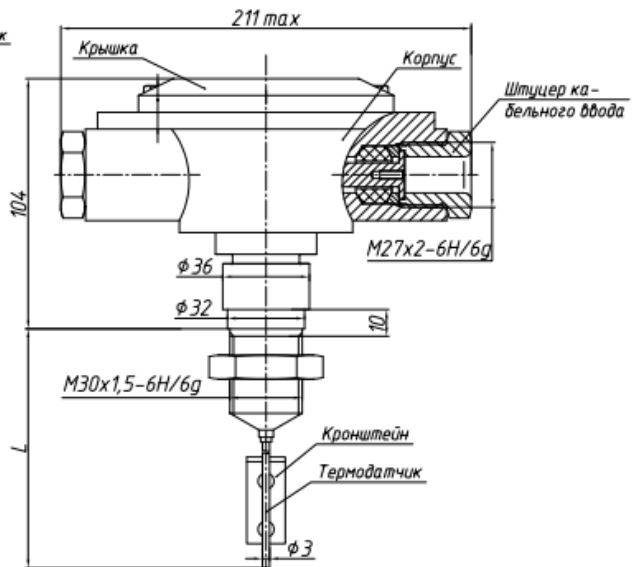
Извещатель пожарный ИП102-1В-НС, монтаж на стену, вариант для открытой прокладки кабеля (К).
